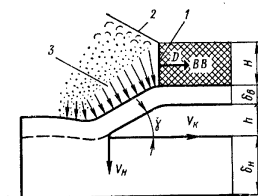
Схема установившегося процесса сварки взрывом:
